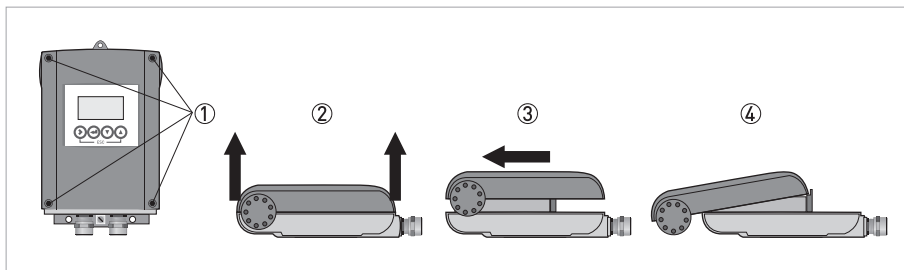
Öffnen und Schließen des Aluminiumgehäuses
